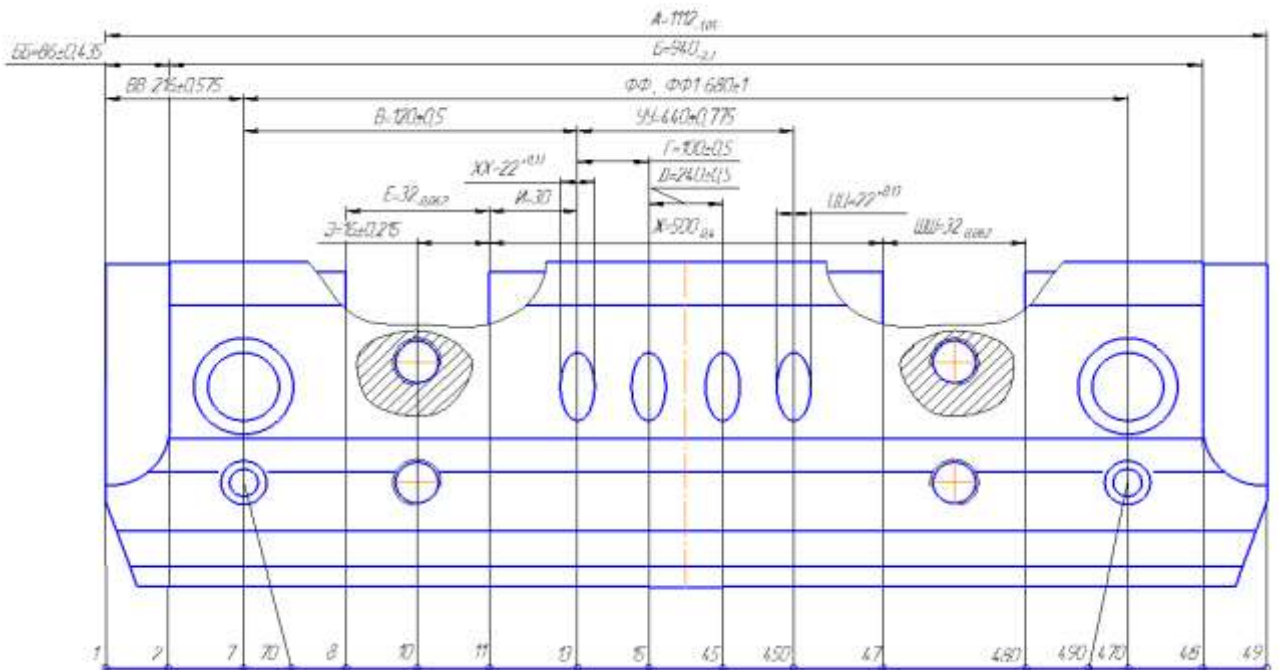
Преобразованный чертеж детали во второй проекции
